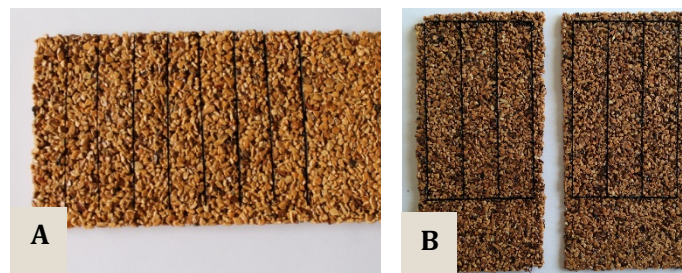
A. Probeta prueba corte láser; B. Probetas corte láser.
